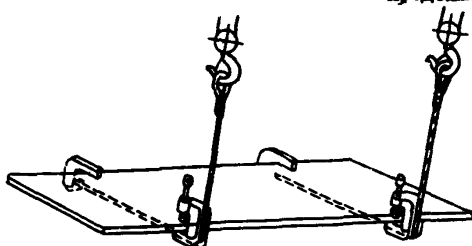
Кантовка крупногабаритных листовых деталей стропами с винтовыми зажимами
